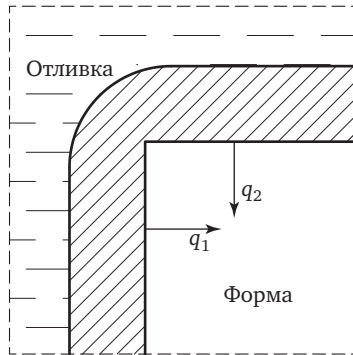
Схема затвердевания металла в наружном углу отливки
